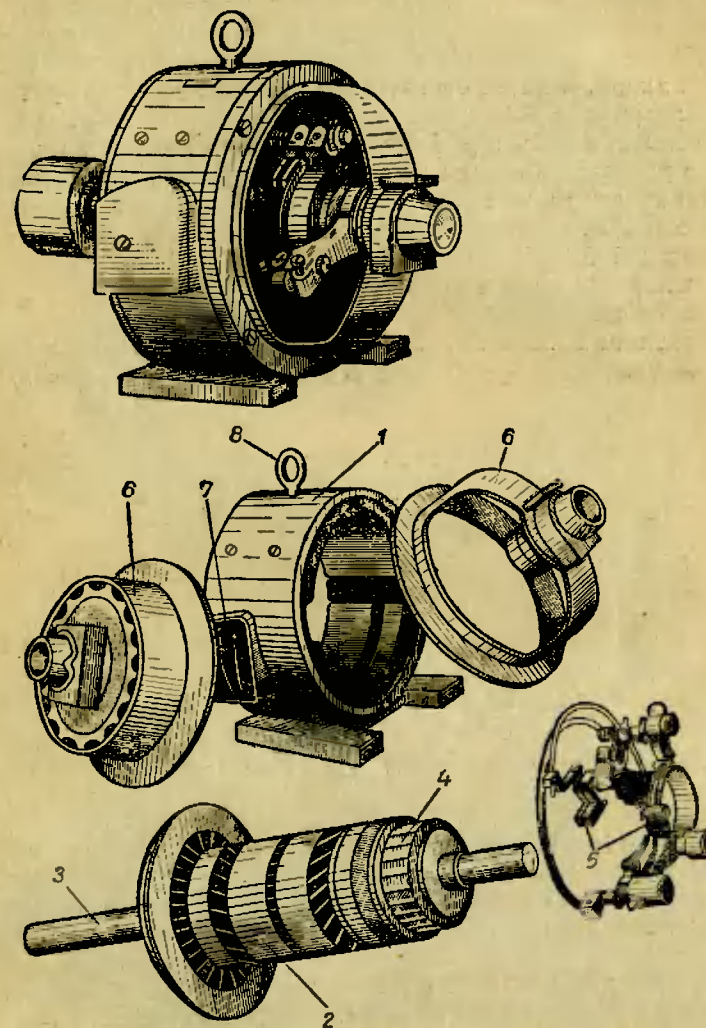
Машина постоянного тока и ее части: 1 — станина индуктора, 2 — якорь, 3 — вал якоря, 4 — коллектор, 5 — траверза со щеткодержателями, 6 — боковые крышки, 7 — выходные зажимы, 8 — кольцо для транспортировки машины.
